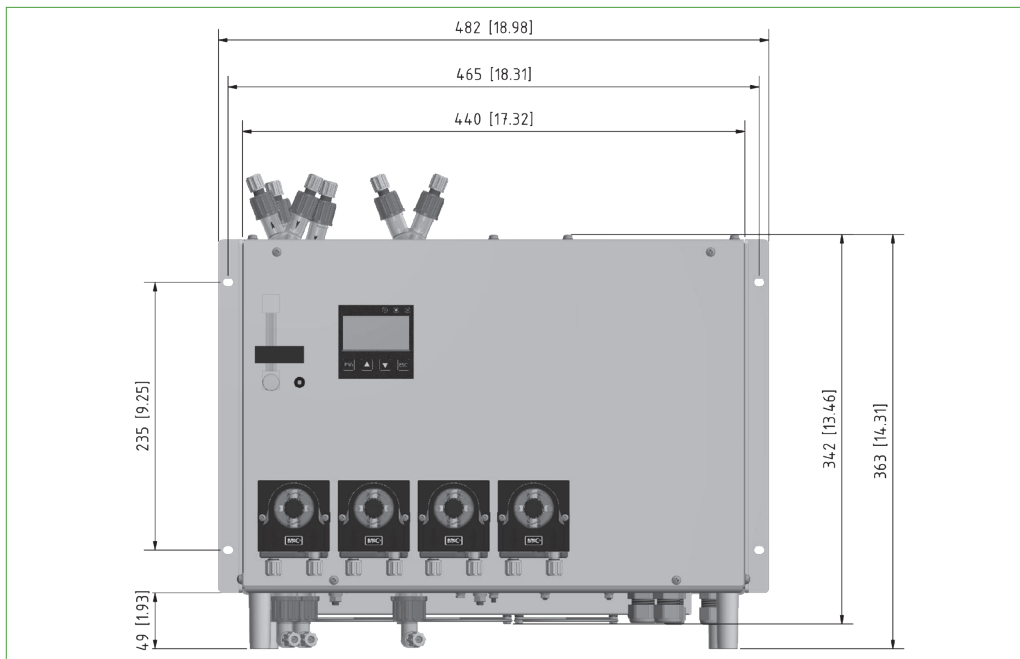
Frontseite: Abmessungen incl. optionaler Schlauchpumpen
